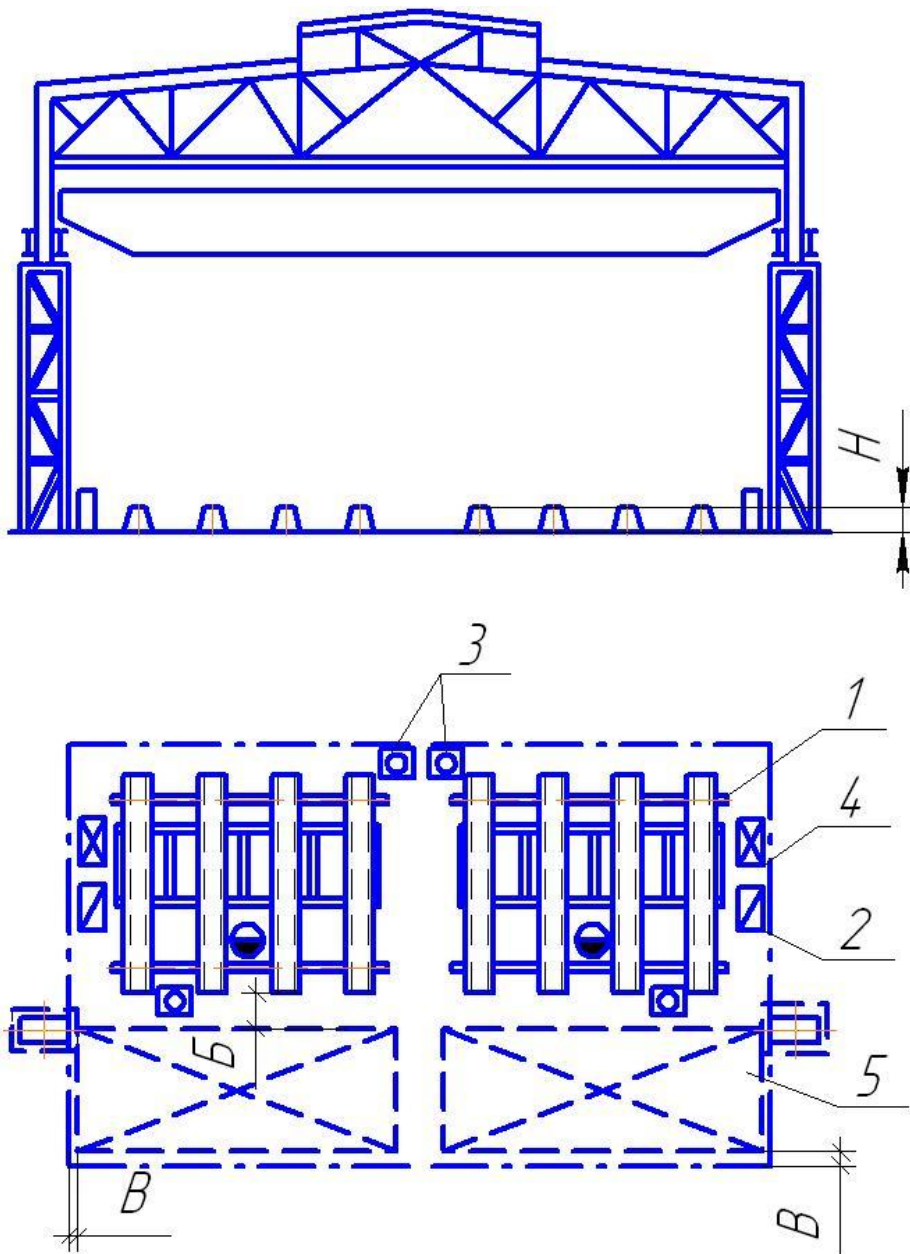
Размещение участка для сварки конструкций с использованием сборочного стенда из козелков:
